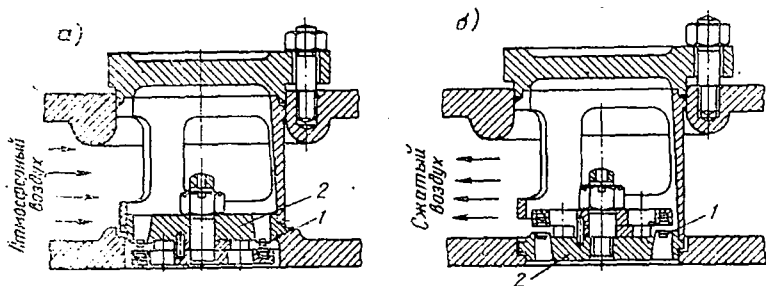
Кольцевой пластинчатый самодействующий клапан
